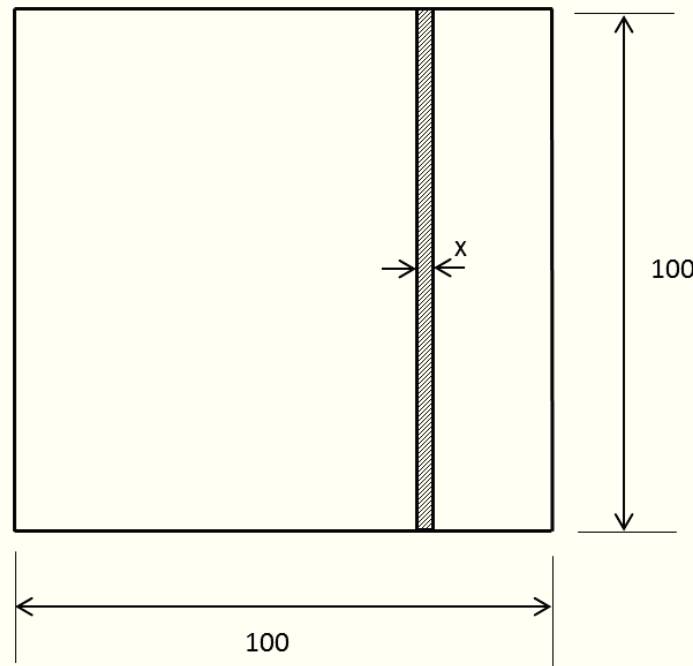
Dimensões do provete utilizado para ensaio de impacto
